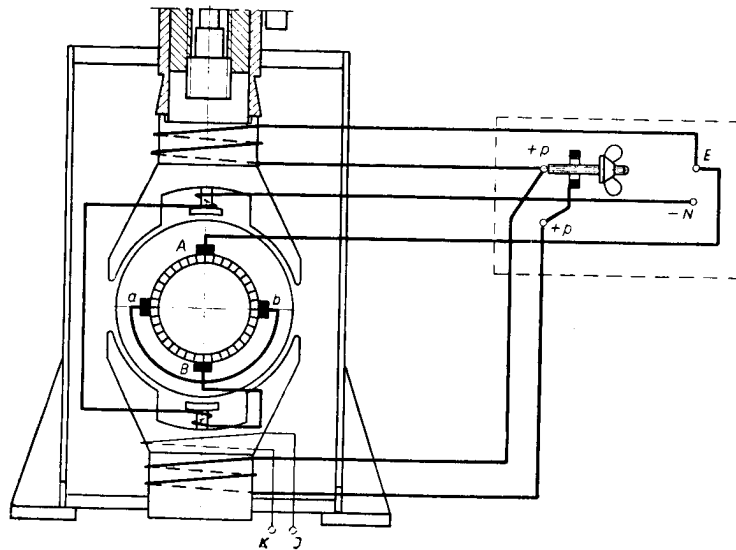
Aufbauskizze des Schweissgenerators
